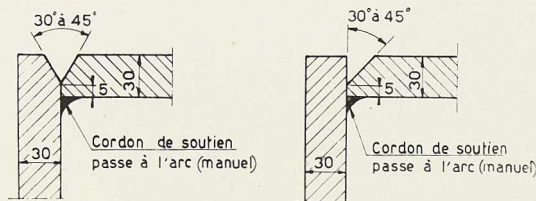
Préparations pour la soudure d'angle de tôles de 30 mm d'épaisseur.
